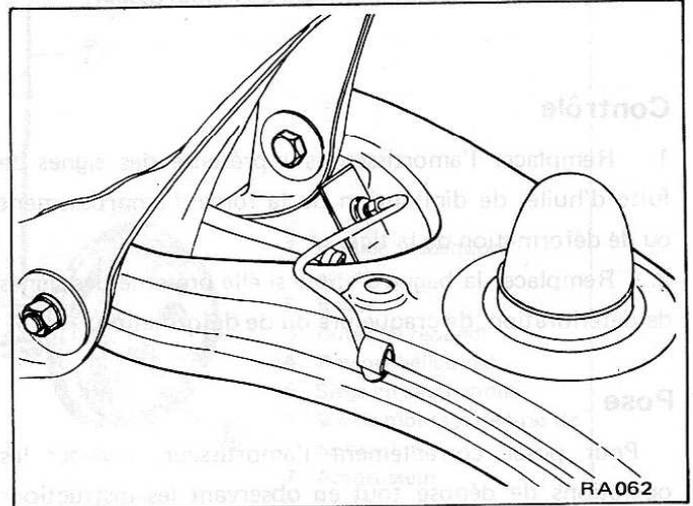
Dépose du bras de suspension arrière par dévissage des deux boulons de montage
